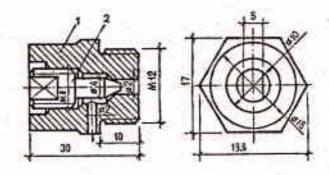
Бессальниковый воздушный кран с поворотным игольчатым штоком:
